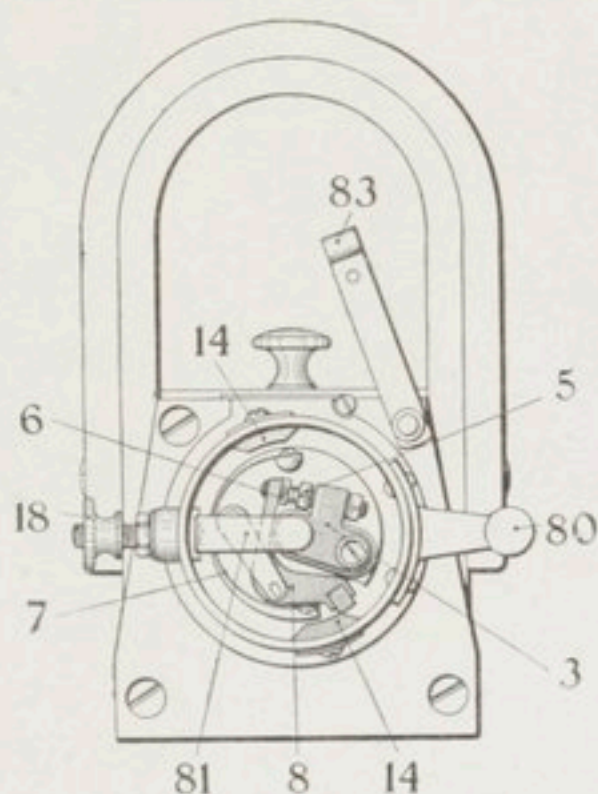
Vue arrière de magnéto Bosch pour moteur à deux cylindres.
